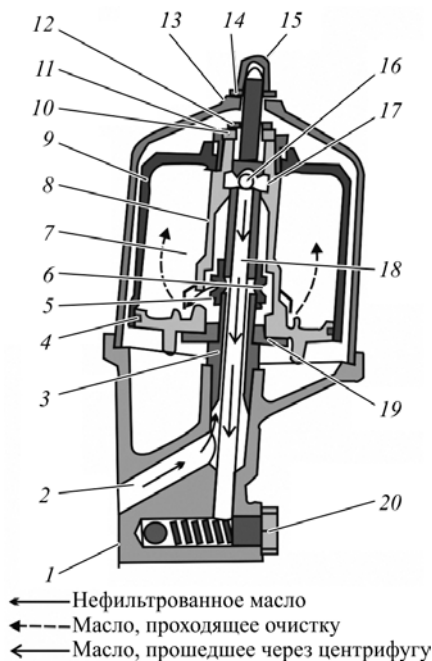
Реактивная центрифуга дизеля Д-240: 1 – корпус центрифуги; 2 – подводящий канал; 3 – ось ротора; 4 – резиновое кольцо; 5 – выходные отверстия; 6 – насадка; 7 – внутренний стакан; 8 – остов ротора; 9 – верхняя крышка ротора; 10 – гайка специальная; 11, 14 – шайбы; 12 – гайка; 13 – колпак; 15 – колпачковая гайка; 16 – тангенциальные отверстия; 17 – радиальные отверстия; 18 – маслоотводящая трубка; 19 – нижняя крышка ротора; 20 – сливной клапан
